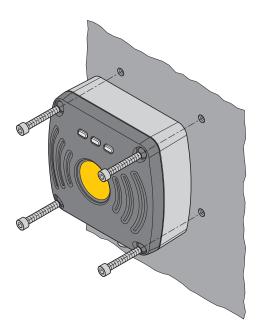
Schreib-Lese-Kopf auf Montageplatte schrauben
